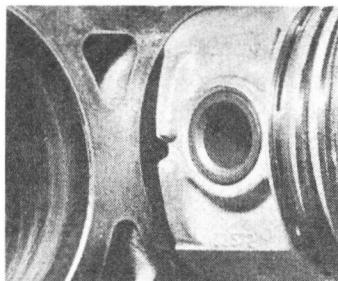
Установите конструкцию поршня/шатуна таким образом, чтобы зарубка на юбке была направлена в сторону крышки приводной цепи
